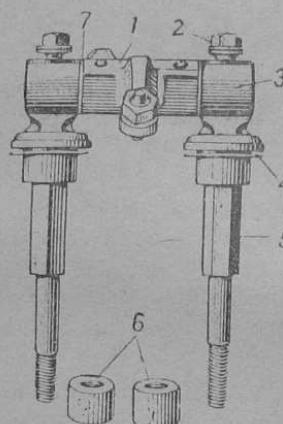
Коромысло двигателя М-76 в сборе с деталями его крепления:
